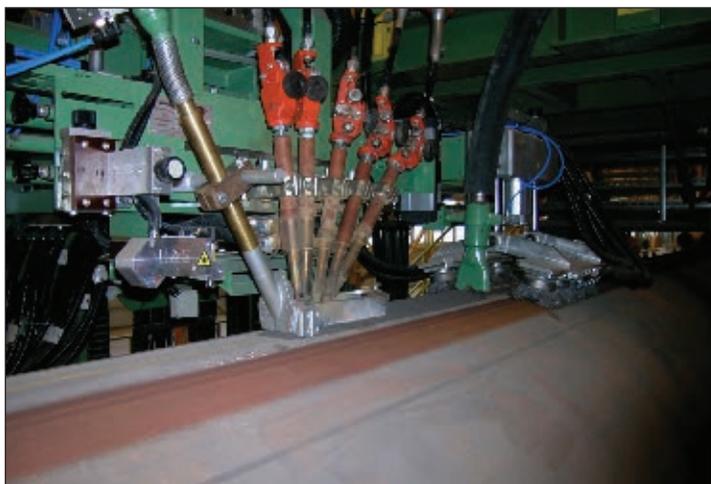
Пятидуговая сварка под флюсом наружного шва
